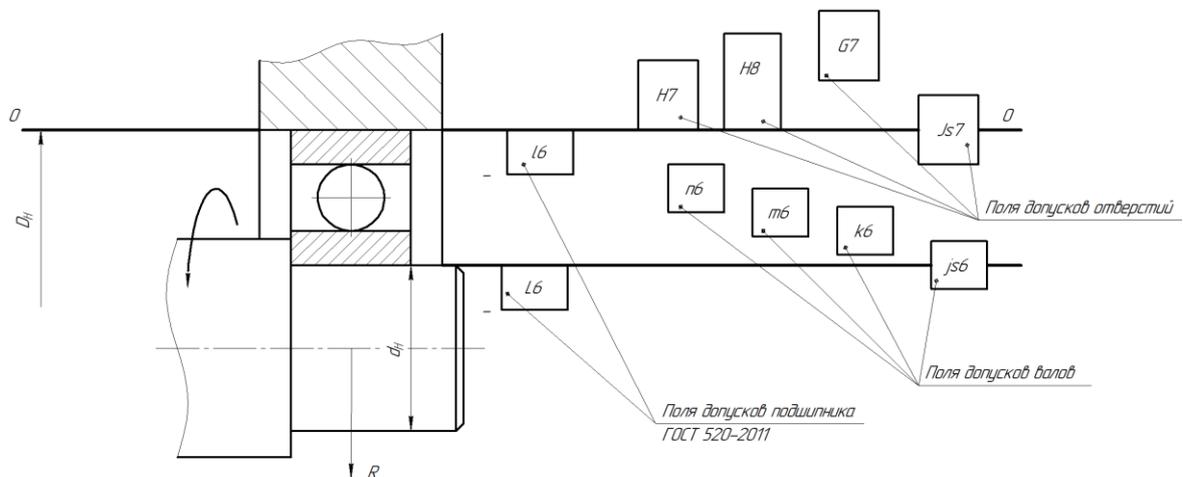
Схема полей допусков подшипника и сопряжённых деталей при вращающемся валу
